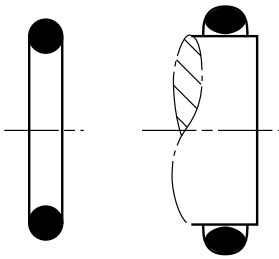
links: ungedehnter O-Ring, rechts: gedehnter O-Ring
